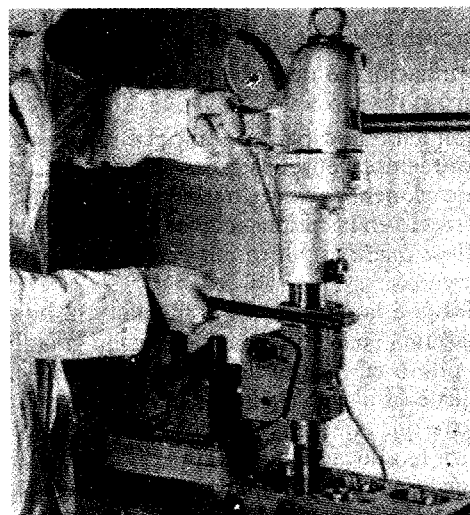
Corte de un rebajo en la culata de cilindros con una máquina instaladora de insertos, para instalar un inserto
